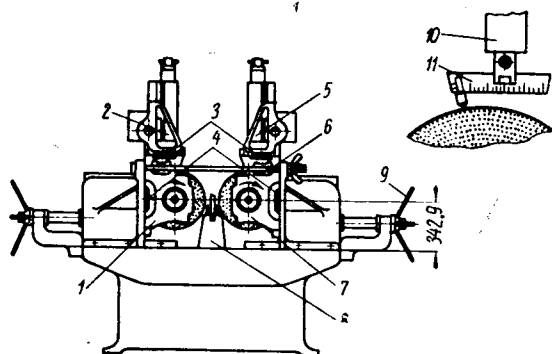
Схема бесцентровополировального станка Цинцинати № 5 (вид со стороны входа деталей):
